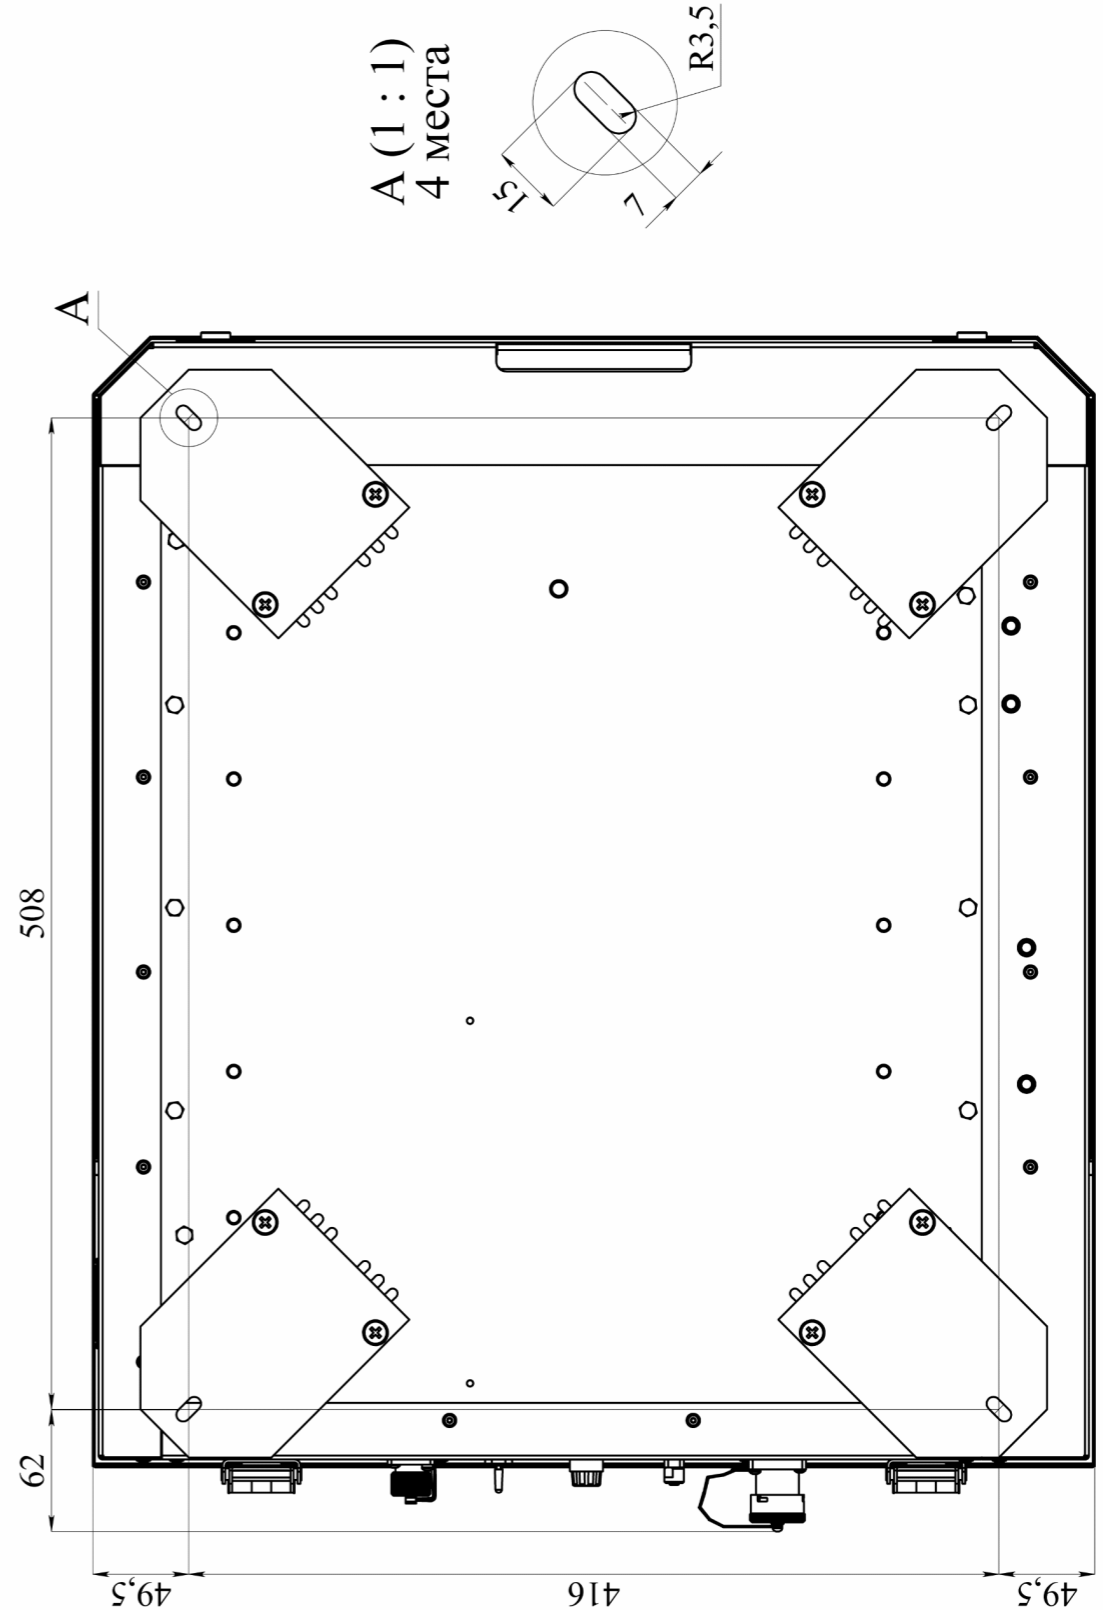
Разметка для крепления амортизаторов УДЦ-Э3 к рабочей поверхности.
